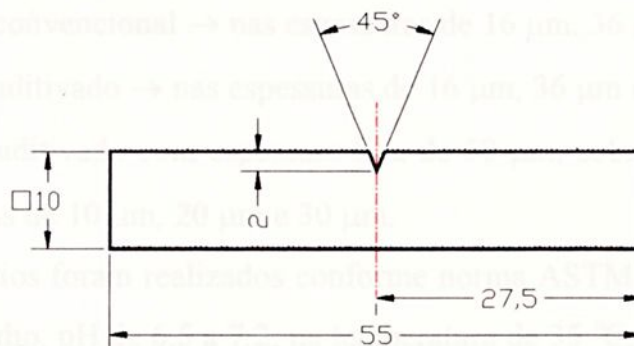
Dimensões do corpo de prova para ensaio de impacto.
